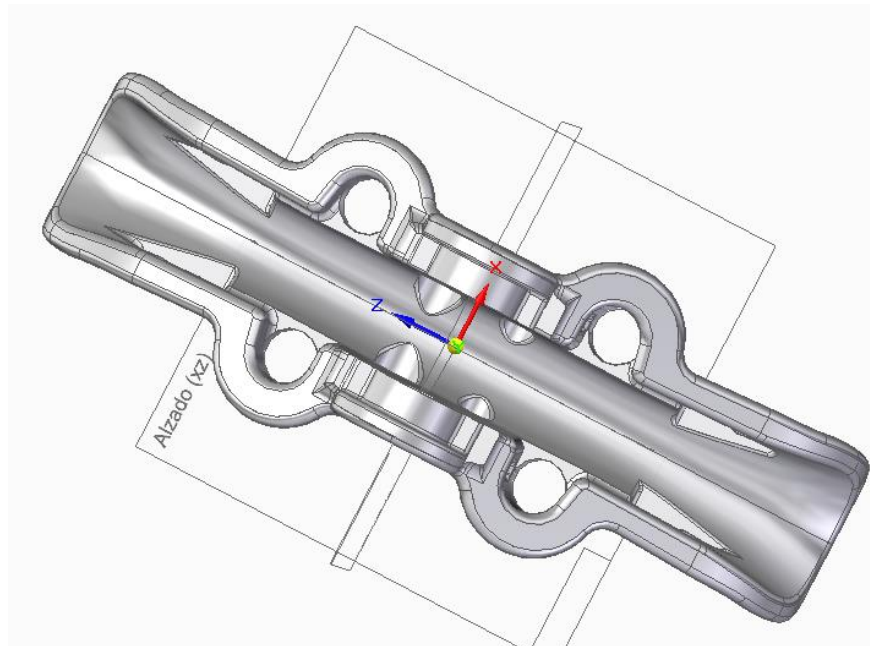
Planta pieza original modificada. Fuente: elaboración propia
